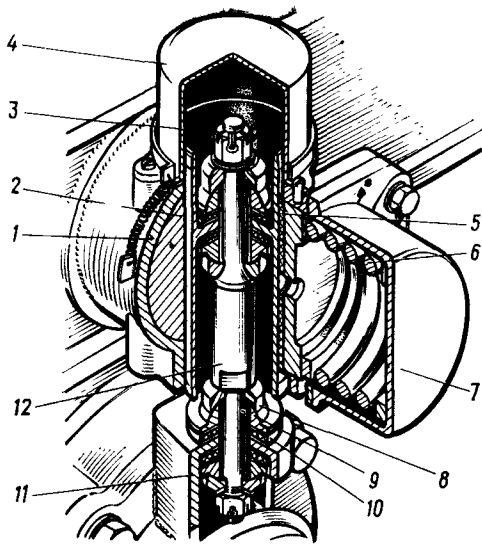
Фрикционный гаситель колебаний: 1 — корпус; 2 — вкладыш; 3 — поршень; 4 — кожа; 5 — фрикционная накладка; 6 — пружина; 7 — крышка; 8 — обойма; 9 — сухарь; 10 — резиновый амортизатор; 11 — кронштейн корпуса буксы; 12 — шток
